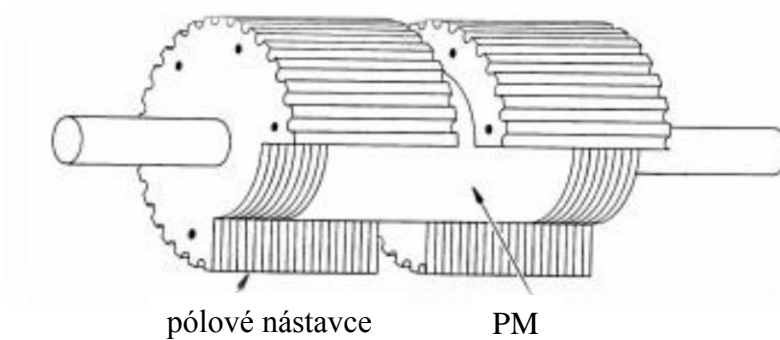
Krokový motor s pasivním rotorem – podle [1]
